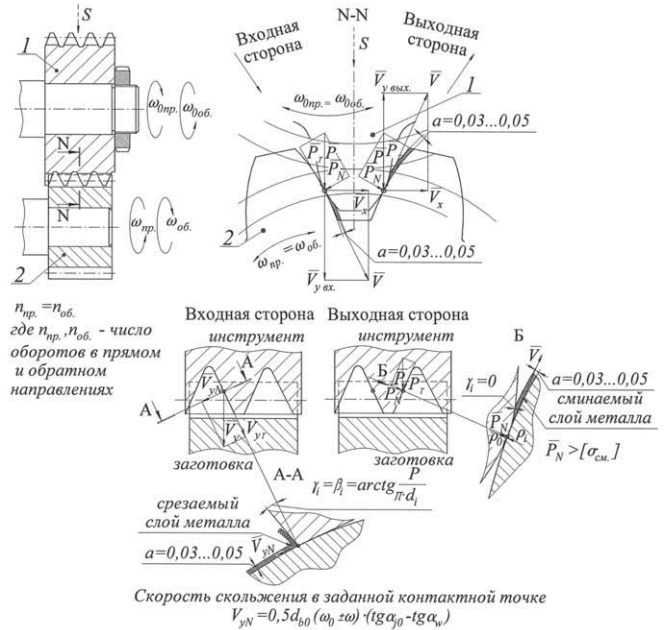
Схема шевингования-прикатывания цилиндрических зубчатых колес (ω , ω_0 – частота вращения обрабатываемой детали и инструмента; S – периодическая подача)
